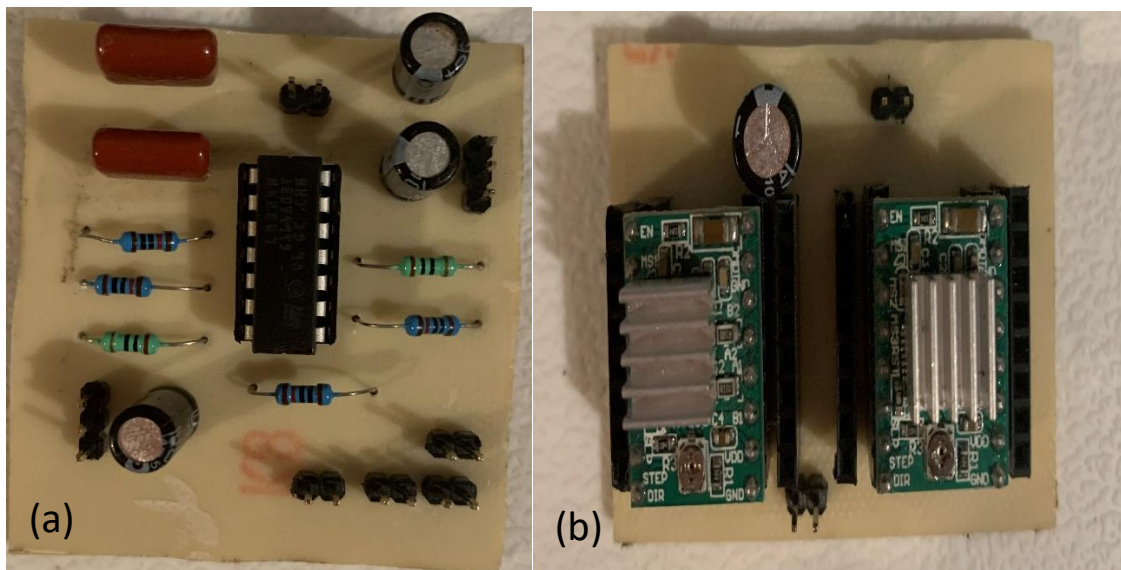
PCB's de (a) adquisición de datos y (b) para el control de los motores a pasos.
